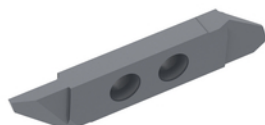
Geometrie VBD typu A, CP-A1108-L3 4325 [16]
